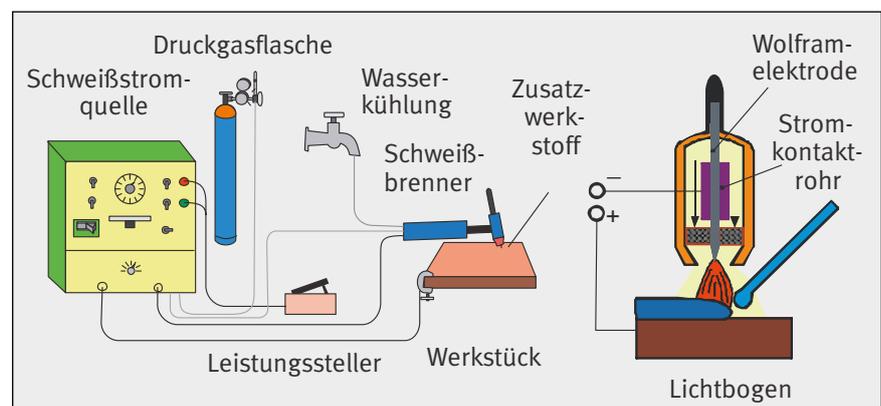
Schweißarbeitsplatz zum WIG-Schweißen: Werkstück, Lichtbogen, Schweißnaht, Zusatzwerkstoff, Gasdüse, Schutzgas, Kontaktrohr, Wolframelektrode, Stromquelle
